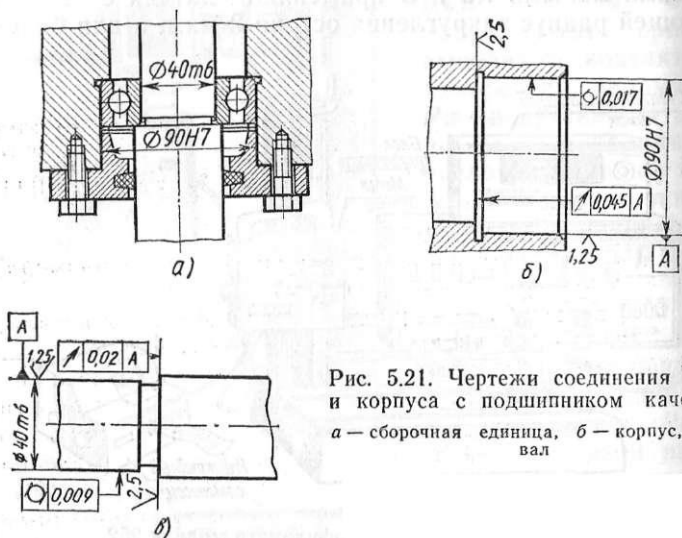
Чертежи соединения вала и корпуса с подшипником качения. а — сборочная единица, б — корпус, в — вал
